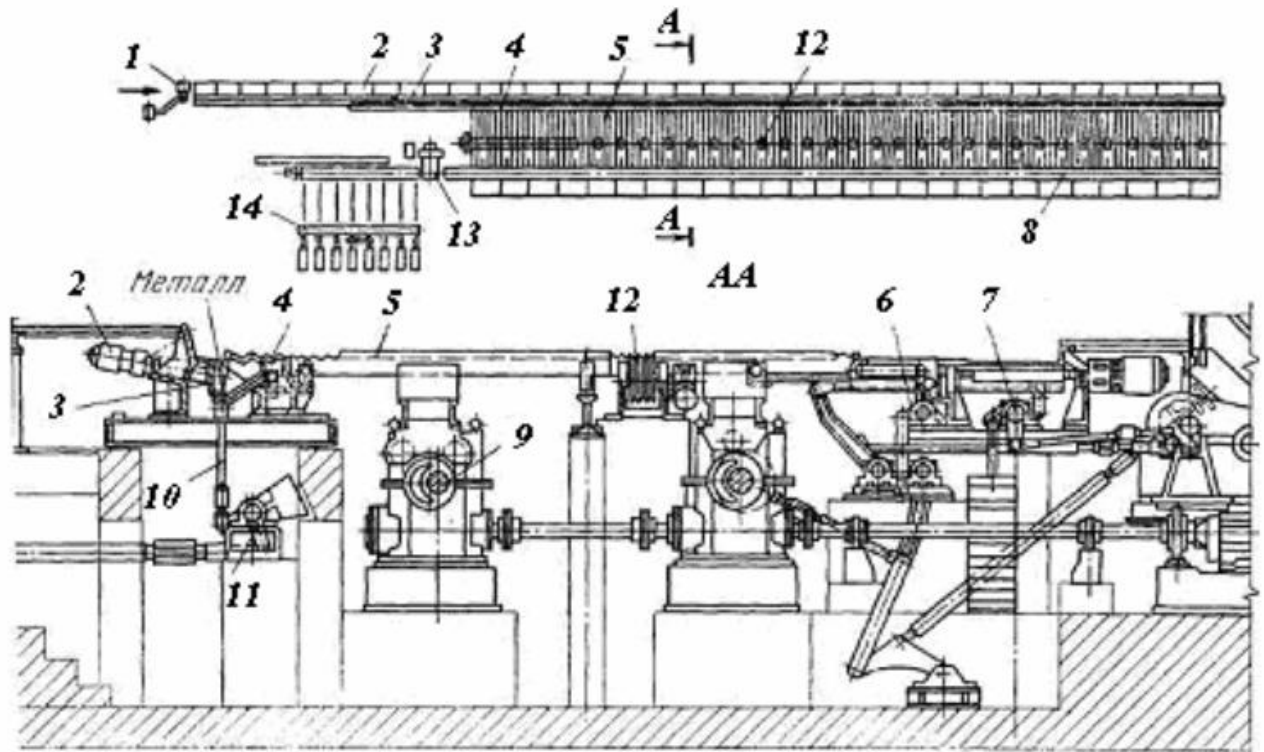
Рейковий холодильник: 1 - летючі ножиці; 2 - підвідний рольганг; 3 - клапани; 4 - гребінки; 5 - система рухомих рейок; 6,7 - пристрої для набору пачок; 8 - відвідний рольганг; 9 - ексцентриковий механізм; 10 - вертикальні тяги; 11 - кривошипно-шатунний механізм; 12 - ролики для вирівнювання смуг; 13 - ножиці; 14 - ваги
